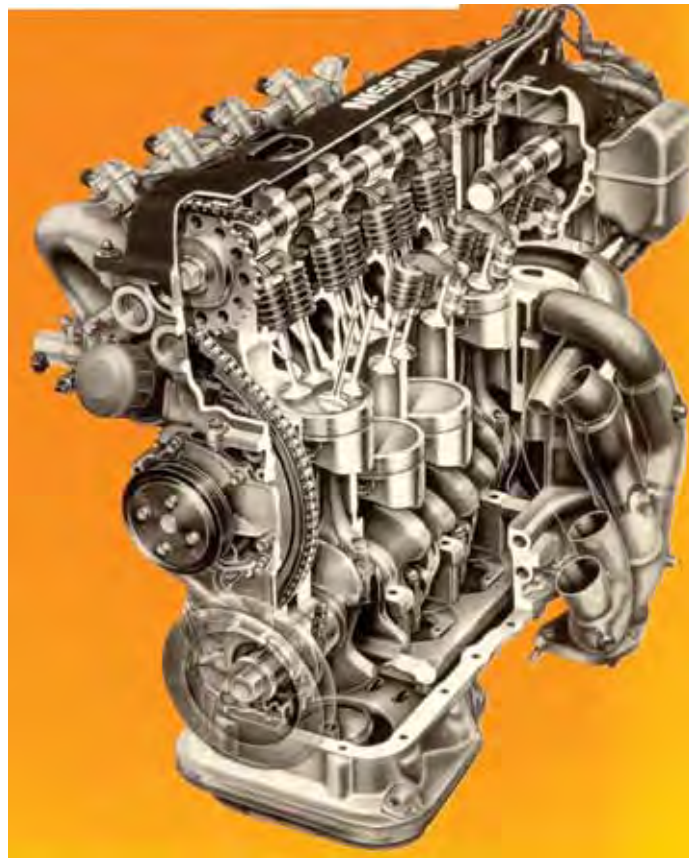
Corte parcial de um motor de 4 cilindros em linha
